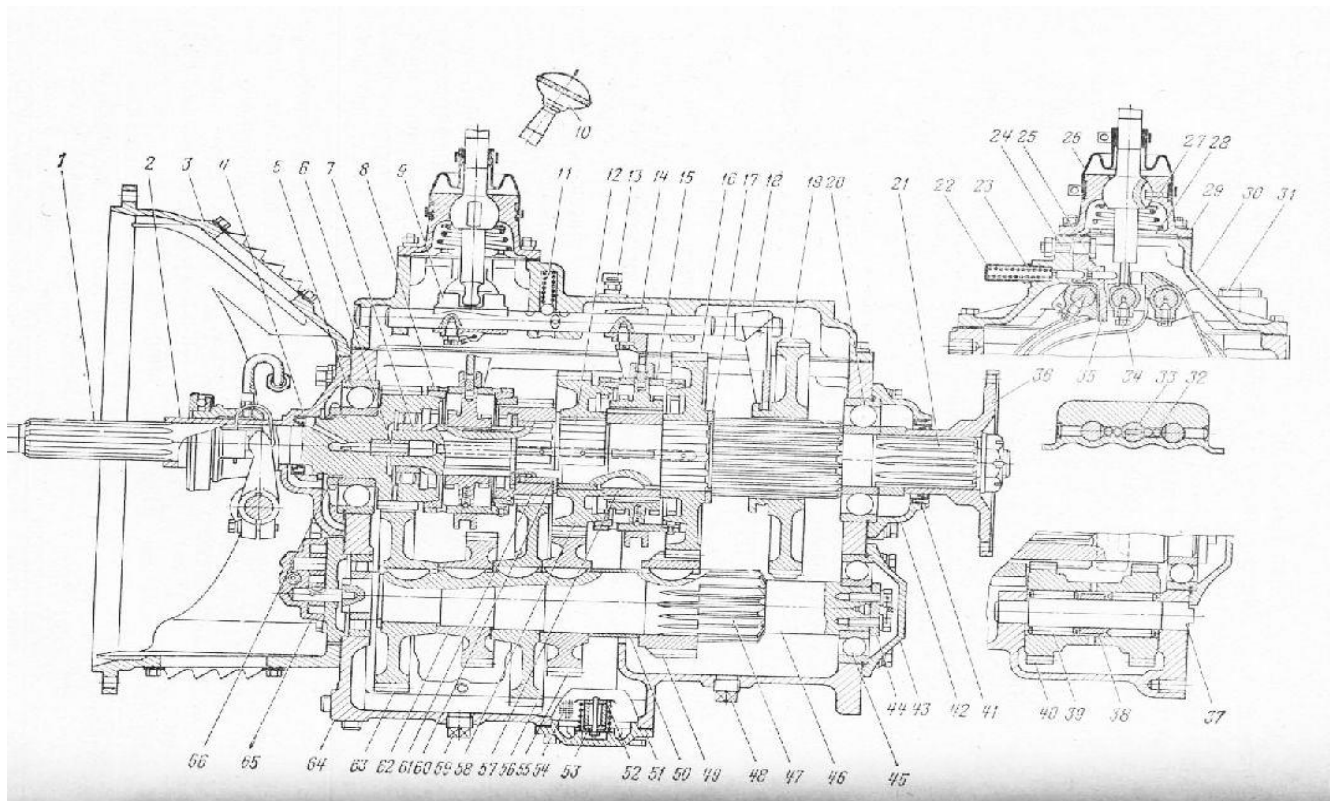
Коробка передач ЯМЗ-236Н:
